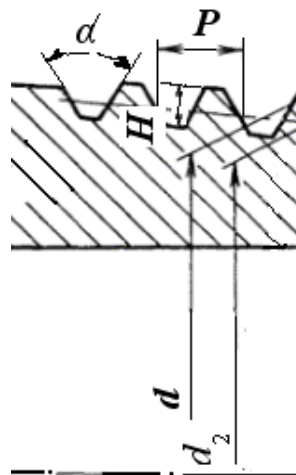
Измеренные параметры резьбы ниппеля резьбового протектора
